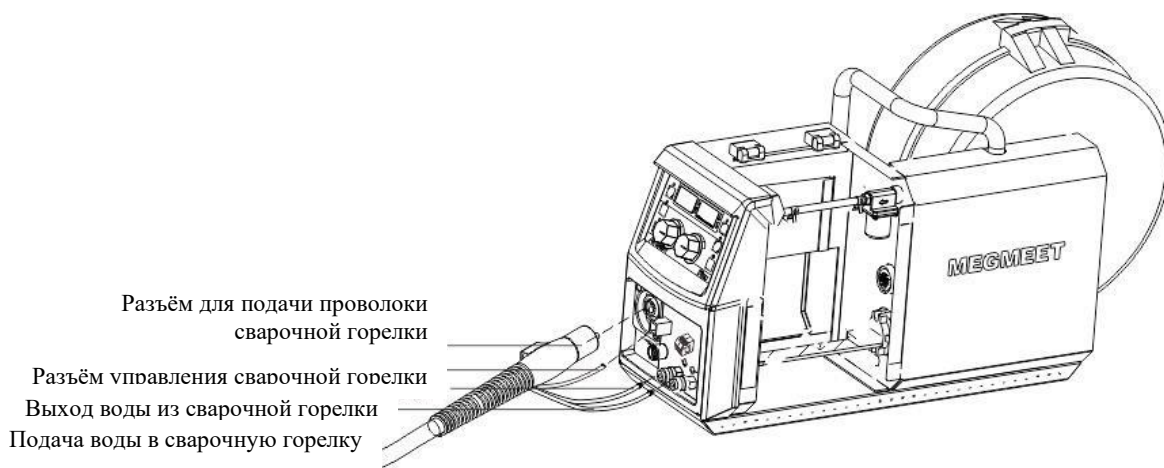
Подключение ручной сварочной горелки
